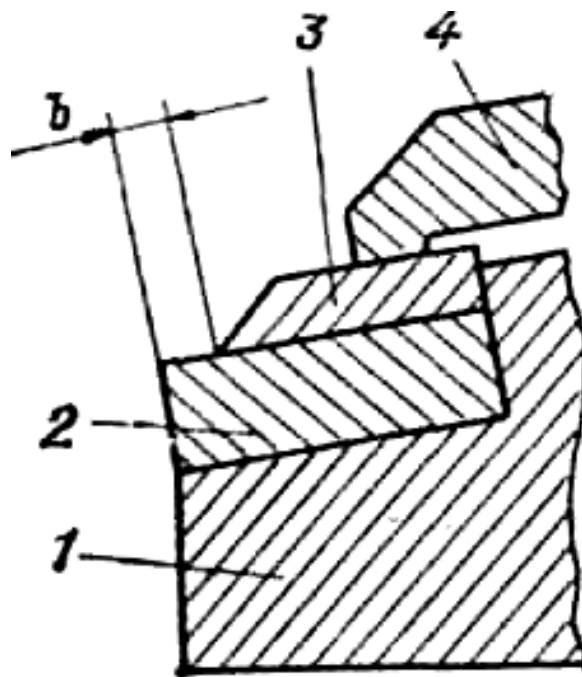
Схема установки стружколома на різці з БНП без отвору:
